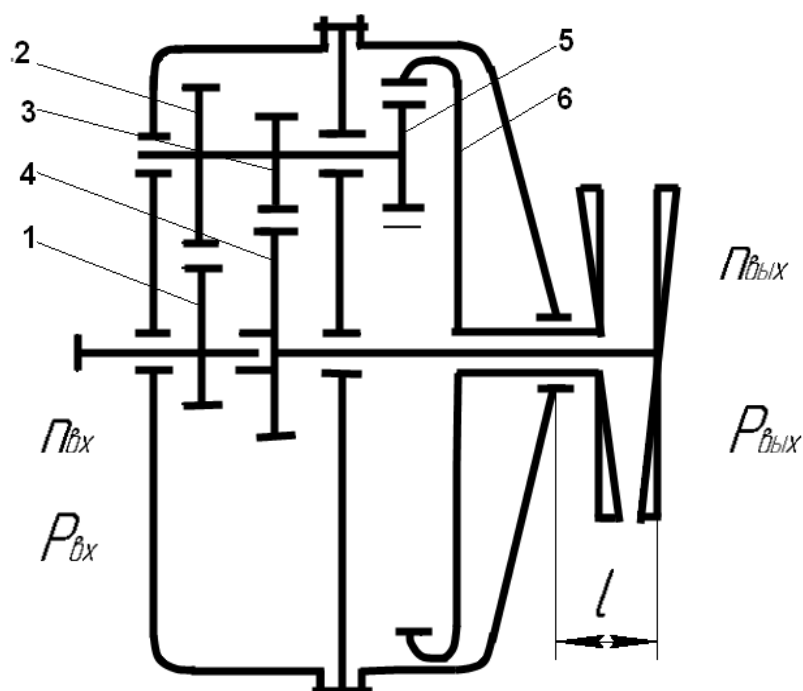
Схема многопоточного редуктора привода соосных винтов ГТД
